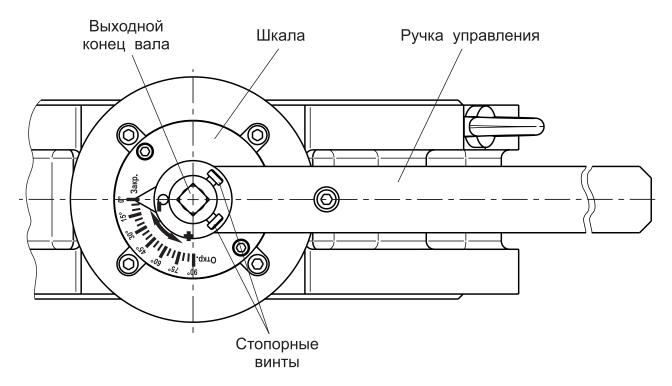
Заслонка регулирующая с ручным управлением (вид сверху)
